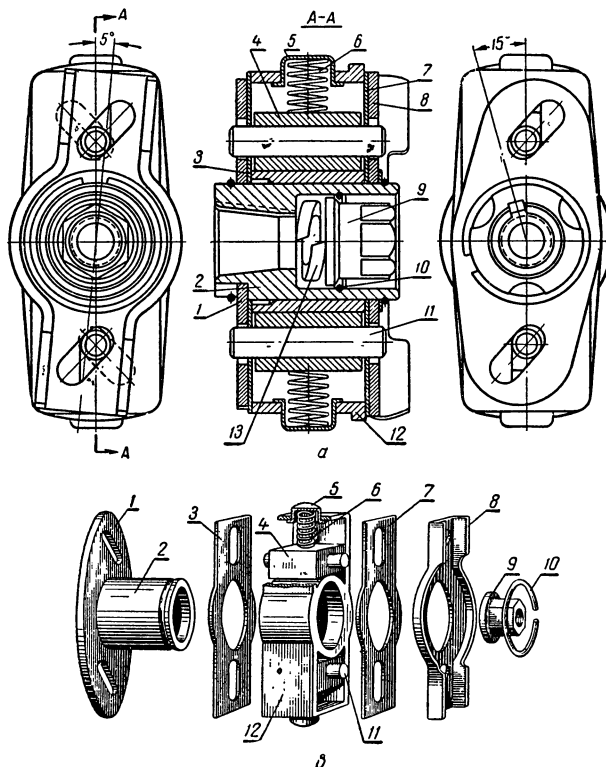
Муфта опережения зажигания MC-22А: а — муфта опережения зажигания MC-22А в сборе; б — детали муфты опережения зажигания; 1 — ведомый диск; 2 — втулка ведомого диска; 3 и 7 — пластинки; 4 — грузики; 5 — колпачок; 6 — пружина; 8 — поводок; 9 — гайка; 10 — стопорное кольцо; 11 — шпилька грузика; 12 — корпус; 13 — пружинная шайба.
